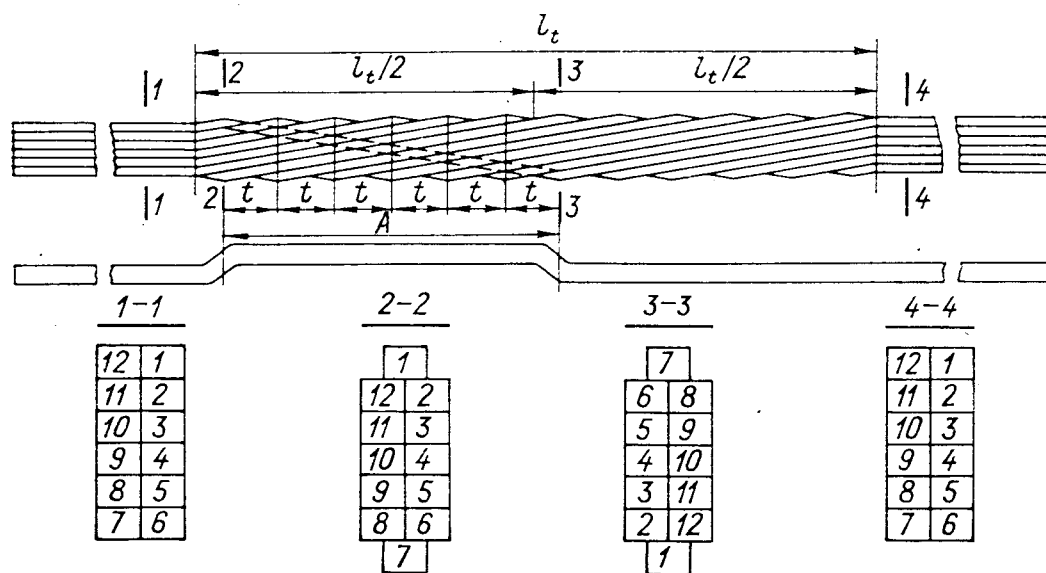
Плетеный стержень обмотки статора (заготовка элементарного проводника и основные размеры)
